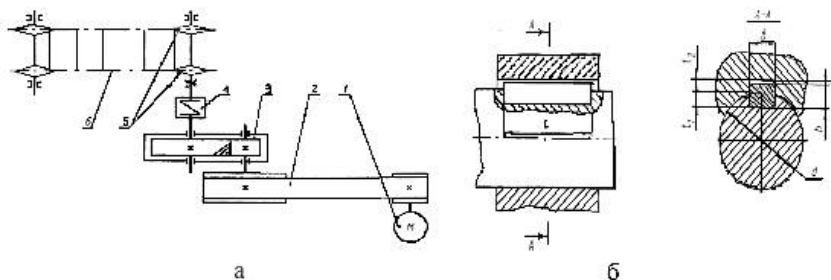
а) 1 – двигатель; 2 – ременная передача; 3 – цилиндрический редуктор; 4 – упругая муфта с горообразной оболочкой; 5 – ведущая звездочка конвейера; б) – тяговая цепь; б) – размеры шпонки
